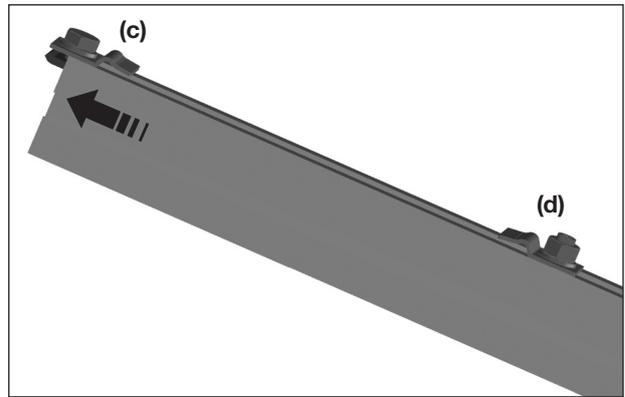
Déplacer la plaque de serrage (c) vers le «haut»
